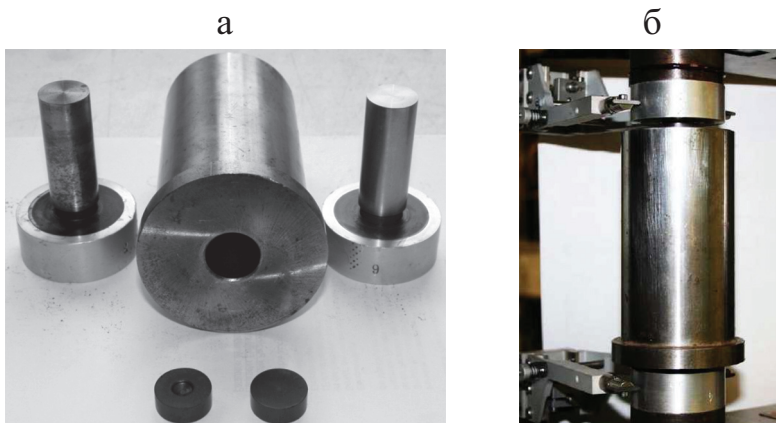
Детали приспособления, образцы и приспособление в сборке с образцами и установленными щупами экстензомера.
